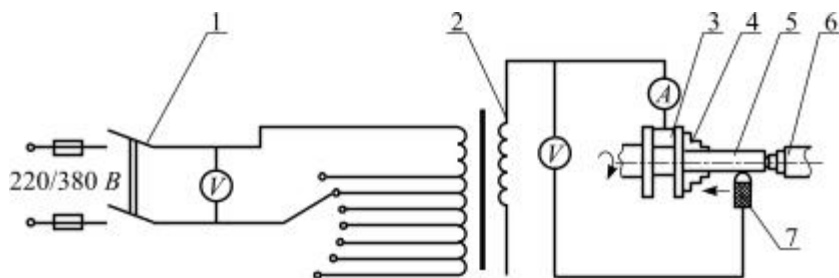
Принципова схема електромеханічної обробки деталі на токарному верстаті: 1 – вимикач; 2 – вторинна обмотка; 3 – струмпідвідний пристрій; 4 – патрон; 5 – деталь; 6 – задня бабка; 7 – тримач з робочим інструментом
